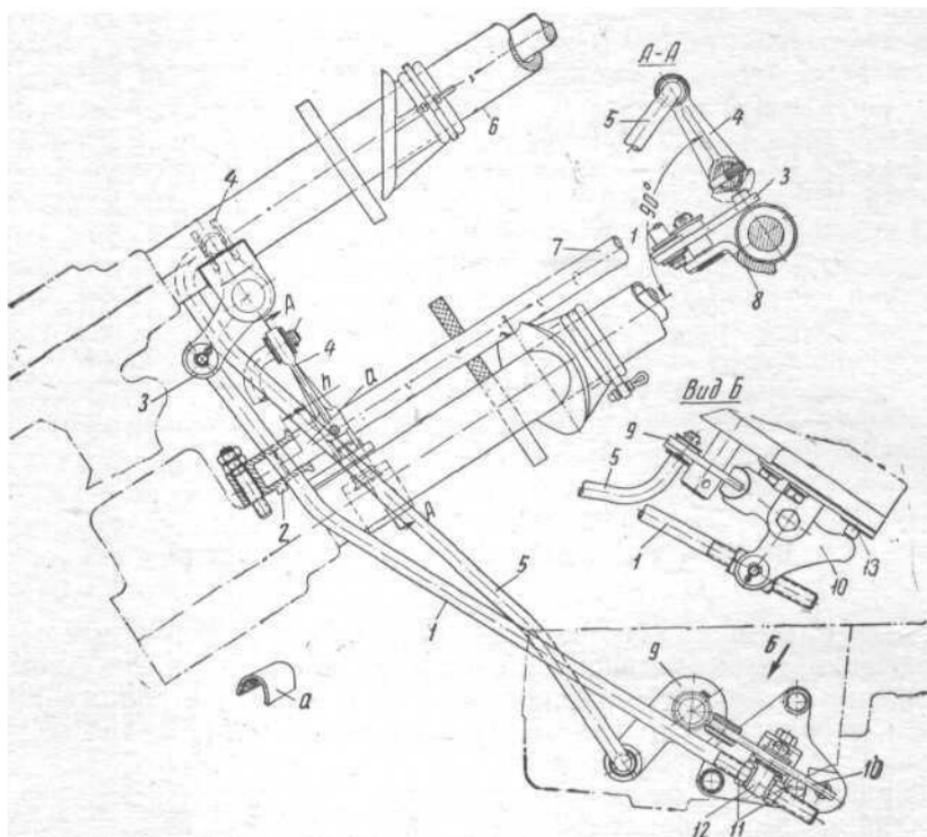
Механизм привода управления коробкой передач модели 407:
